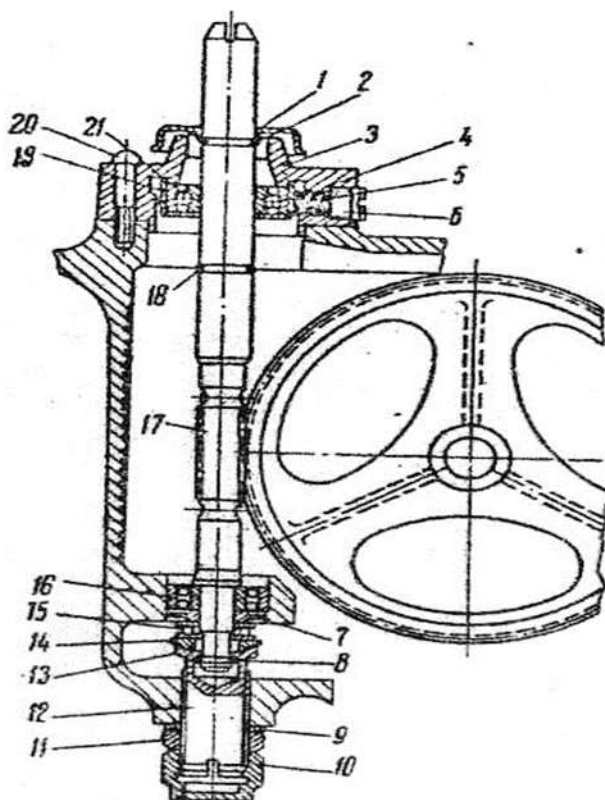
Вертикальный вал сепаратора СОМ-3-1000М:
